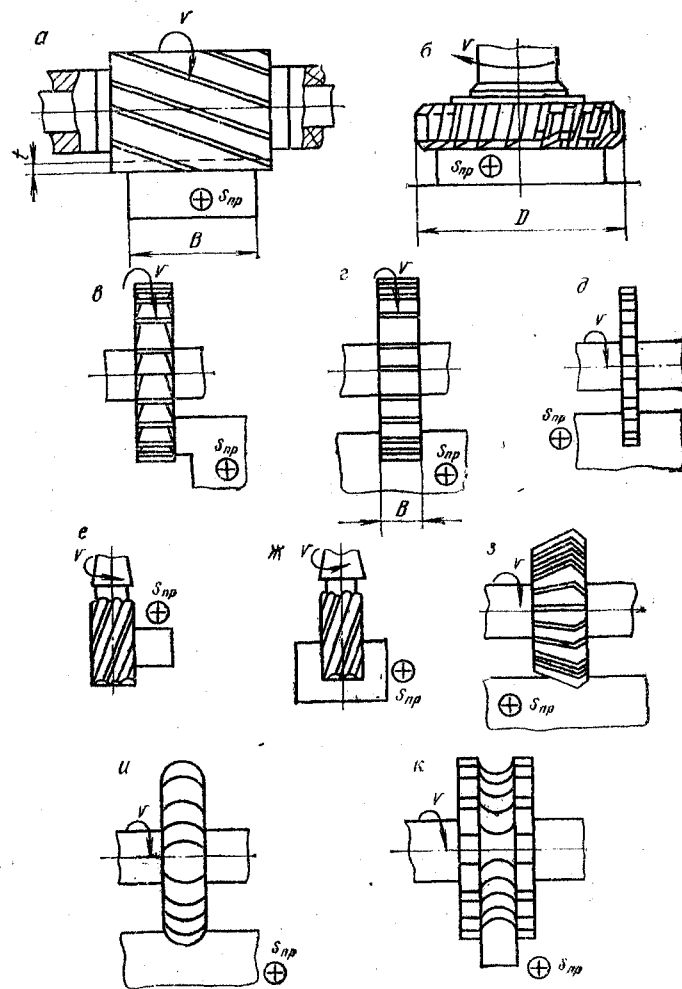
Фрезы и схемы обработки поверхностей и заготовок на фрезерных станках
